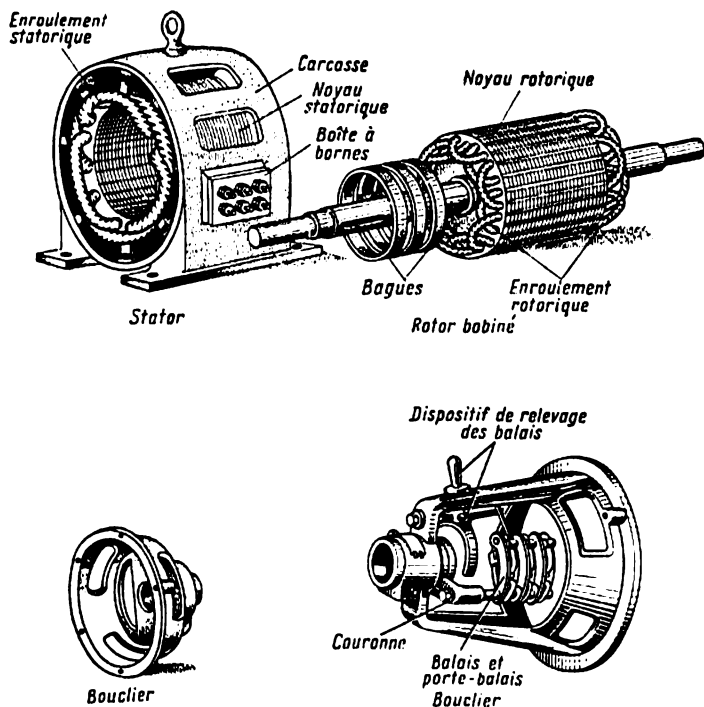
Moteur asynchrone à rotor bobiné démonté
